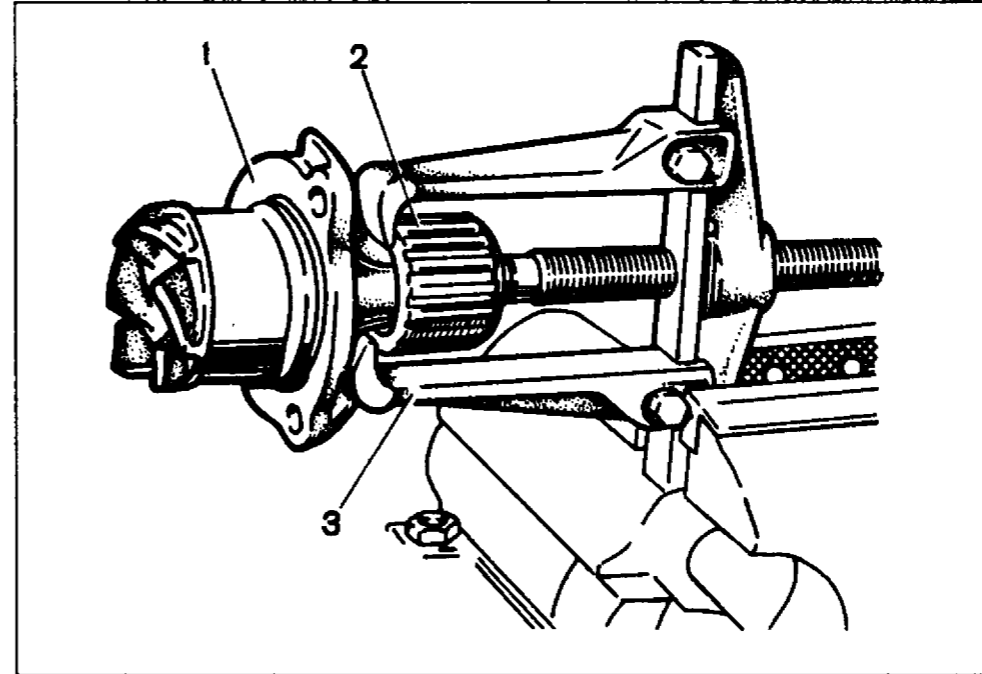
Снятие зубчатого шкива привода насоса: 1 — корпус насоса; 2 — зубчатый шкив; 3 — съемник
